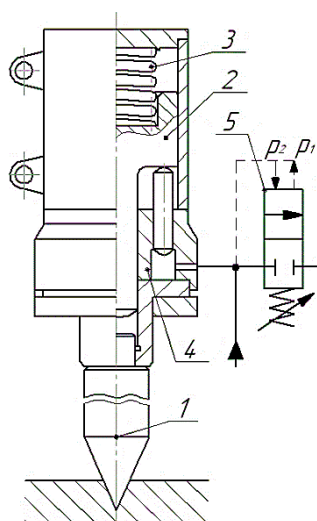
Принципова схема віброударного пристрою на базі гідроімпульсного привода для руйнування гірських порід
